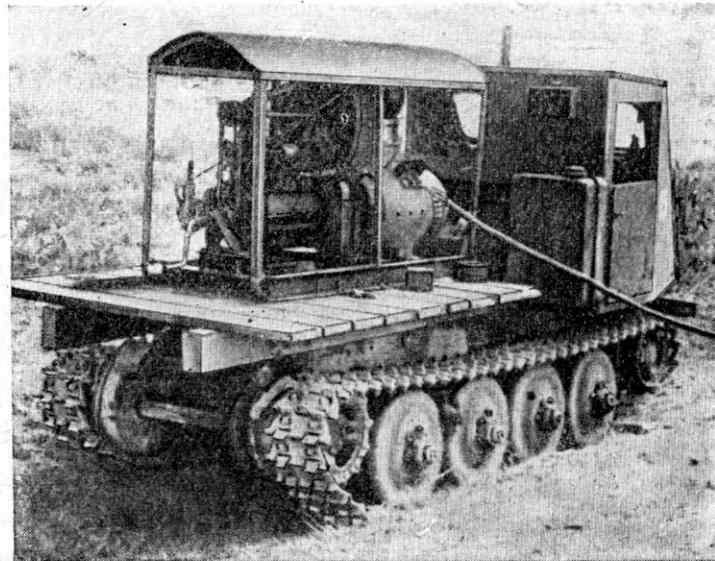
Сварочный агрегат на трелевочном тракторе (Нейский леспромхоз).
